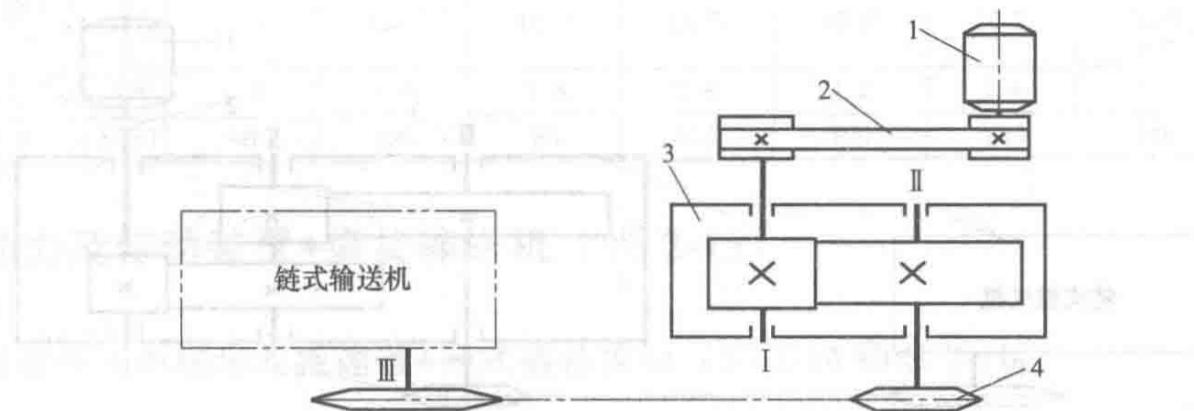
带传动+一级圆柱齿轮减速器+滚子链传动
